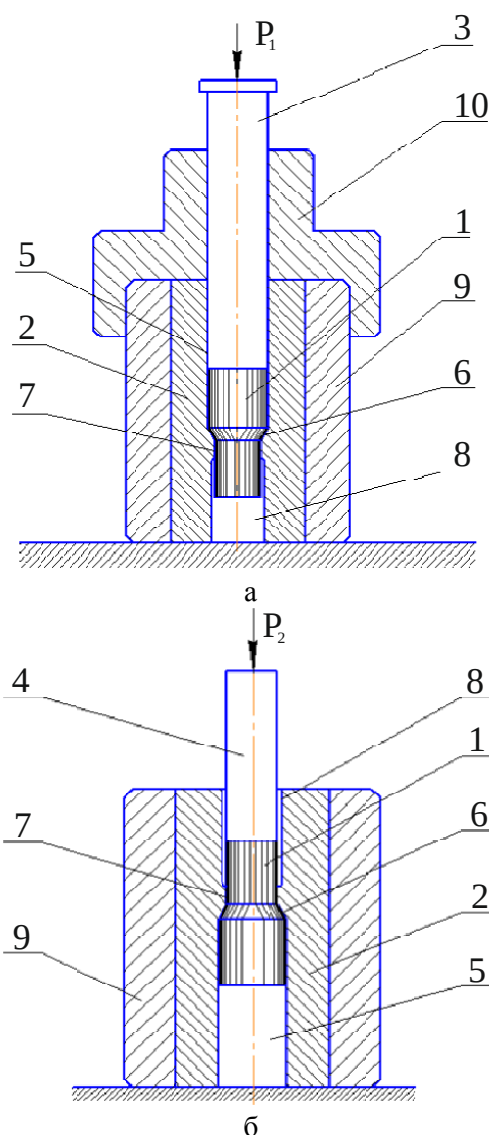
Схемы процессов деформирования (а) в коническом отверстии и выталкивания (б): 1 – заготовка; 2 – матрица; 3 – пуансон; 4 – выталкиватель; 5 – заходное отверстие; 6 – деформирующий конус; 7 – калибрующий пояс; 8 – выходное отверстие; 9 – корпус матрицы; 10 – направляющая пуансона
